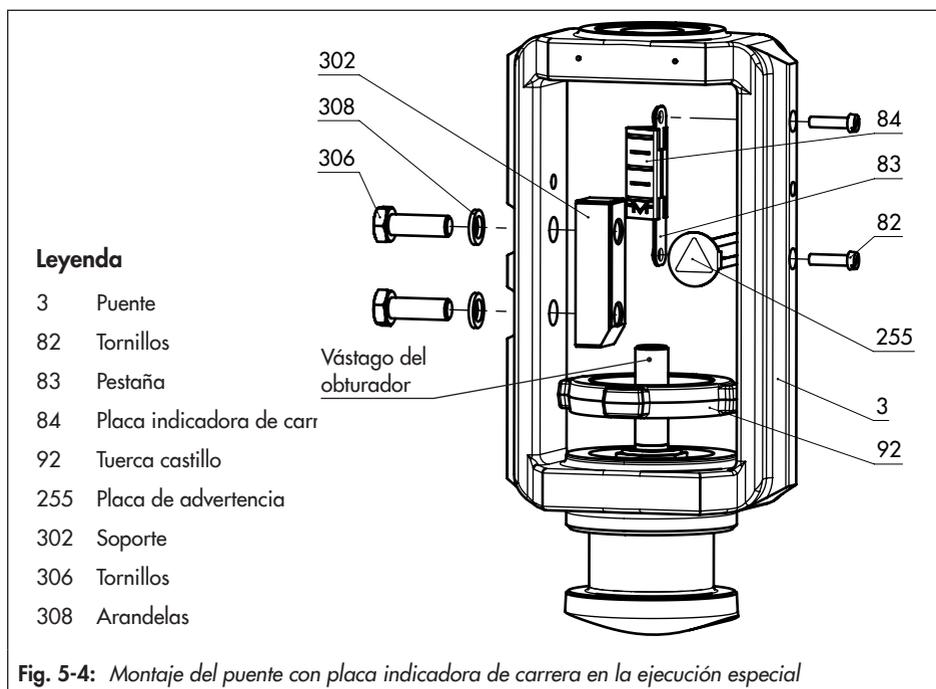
Montaje del puente con placa indicadora de carrera en la ejecución especial
